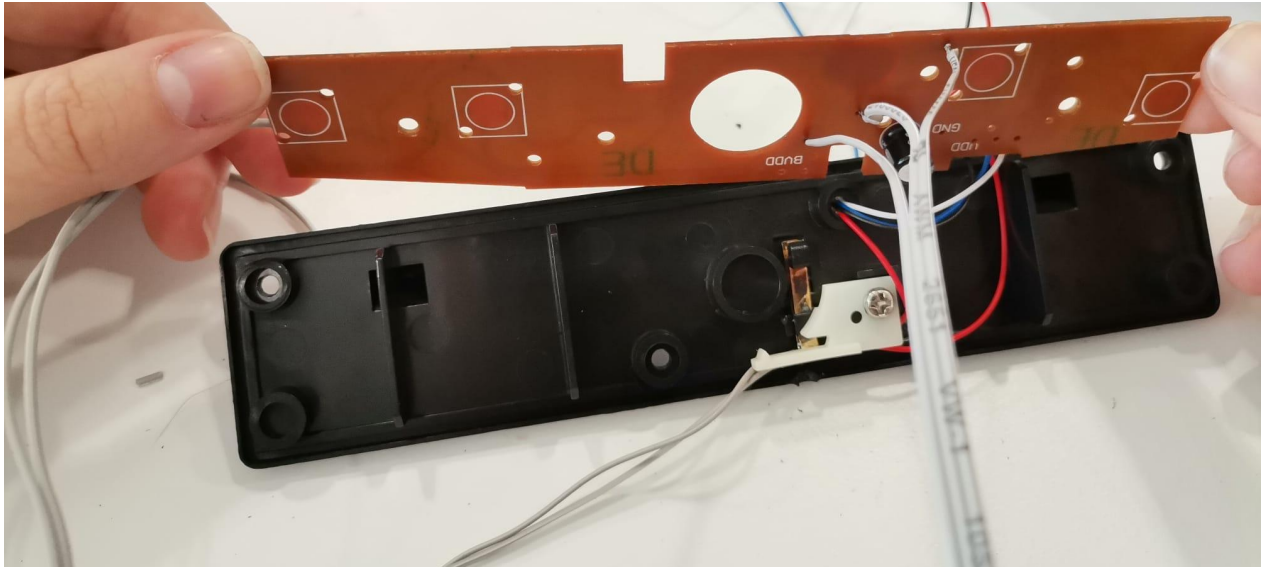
Parte de trás da placa PCB do brinquedo e local do interruptor ligar/desligar
